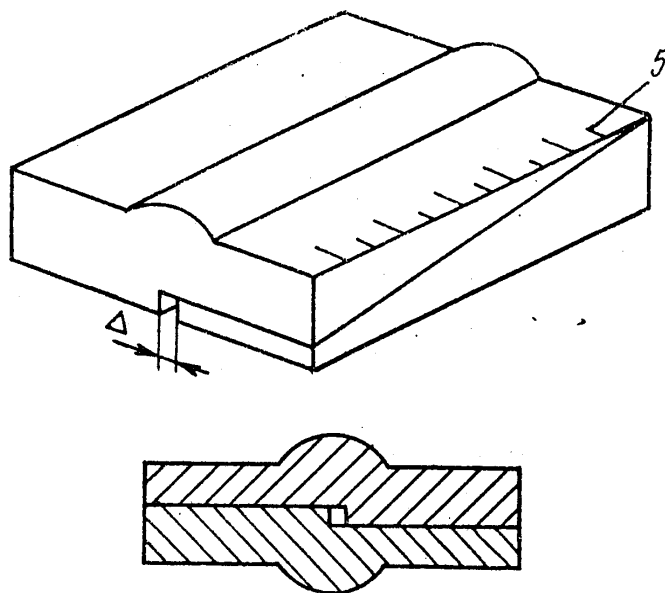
Контрольный образец – имитатор сварного соединения с пластинами клиновидной формы
